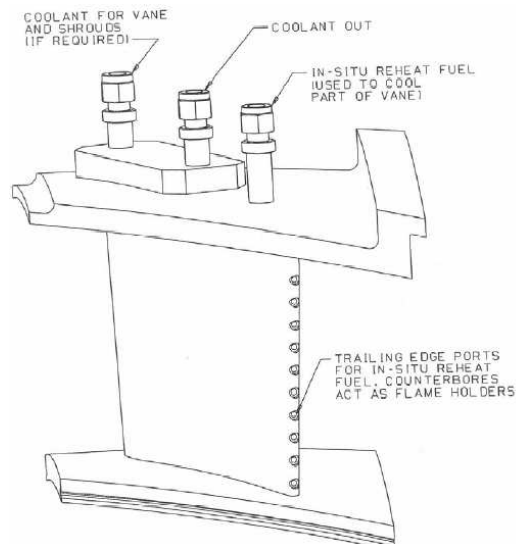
Desenho conceitual de um sistema de reaquecimento *in-situ*, da Siemens Westinghouse.
